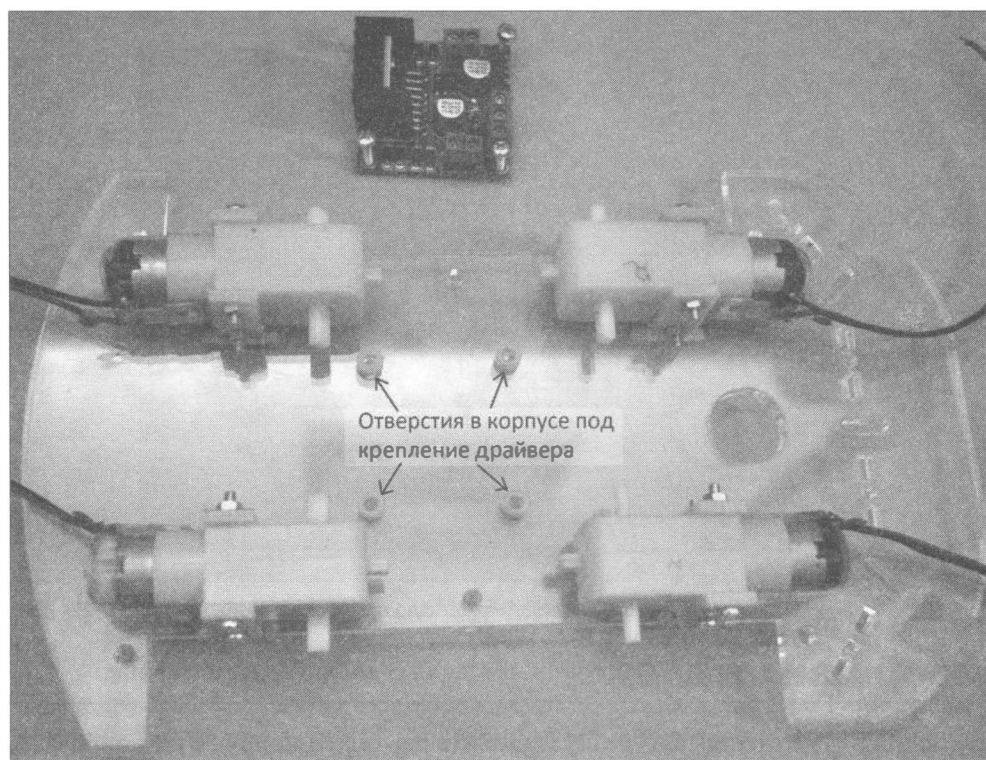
Расположение отверстий для крепления драйвера на корпусе робота
